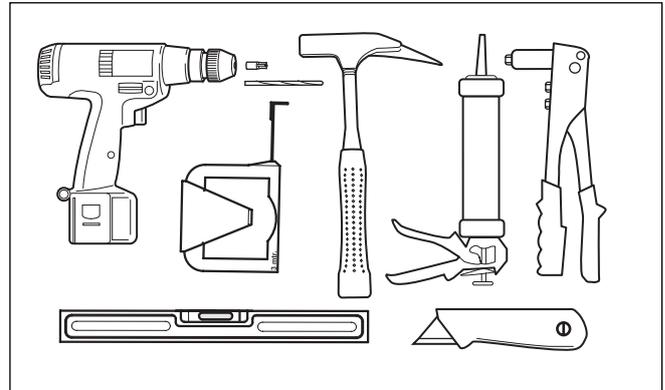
Montage-Werkzeuge: Wasserwaage, Akku-Schrauber, Torx-Bit (TX25, im Lieferumfang enthalten), Bohrer 4,5 mm, Hammer, Maßband/Gliedermaßstab, Gummihammer, Teppichmesser, wetterfestes Silikon und Nietzange (im Lieferumfang enthalten)
